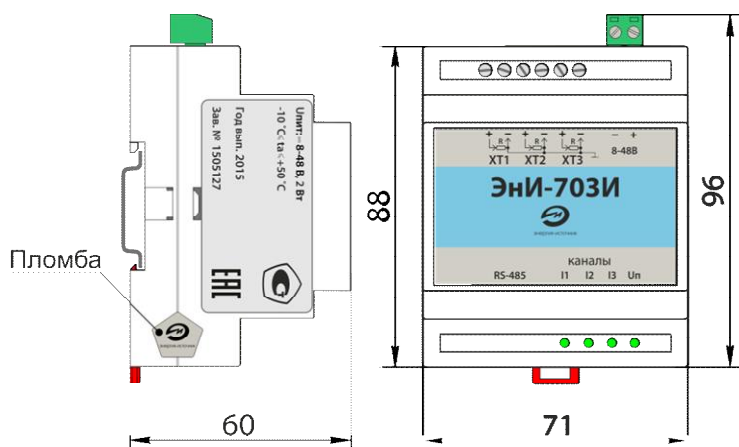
Общий вид измерителя тока ЭНИ-703И
